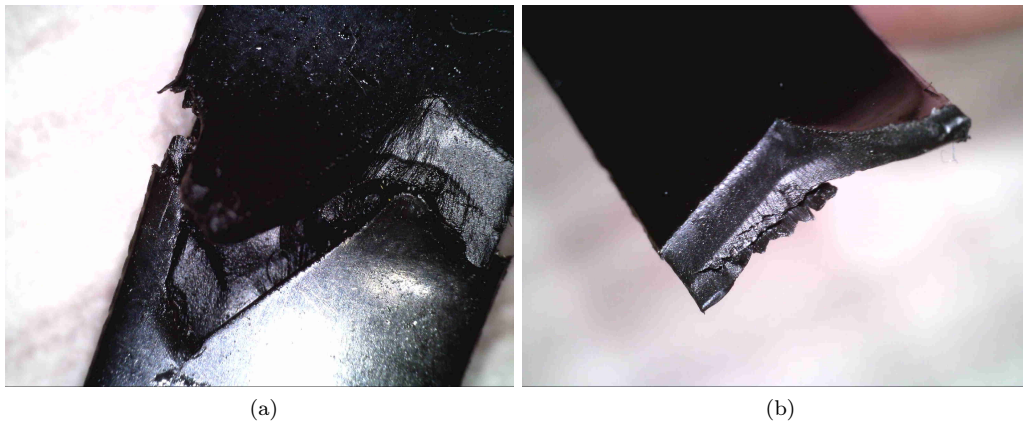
Faciès de rupture en fatigue des éprouvettes obtenues par injection dans un moule
